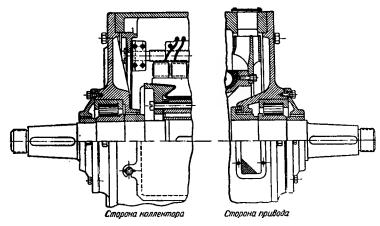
г. Подшипниковые узлы на роликоподшипниках.
